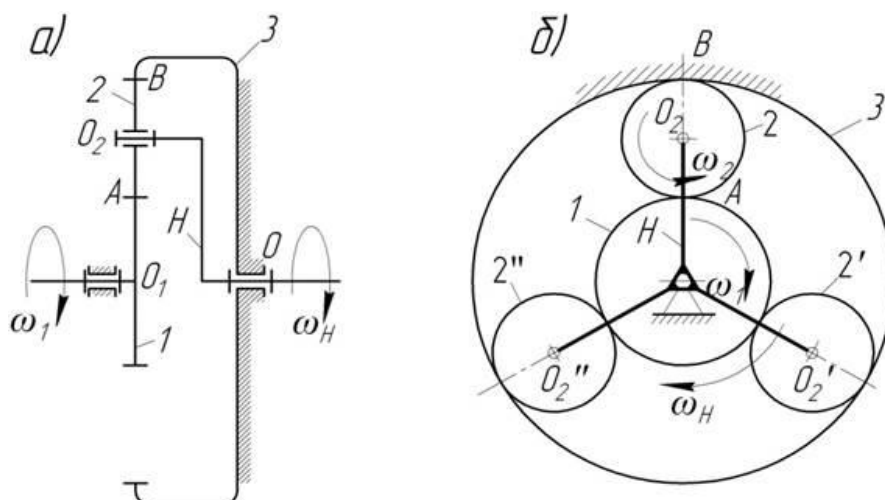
Схема планетарной передачи с одинарными сателлитами
